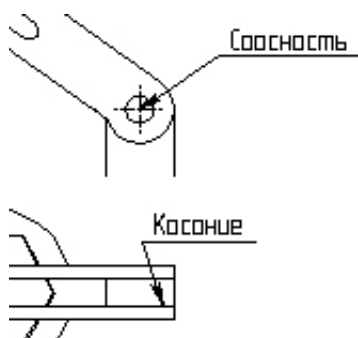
Сопряжение деталей «Корпус» и «Гайка»
